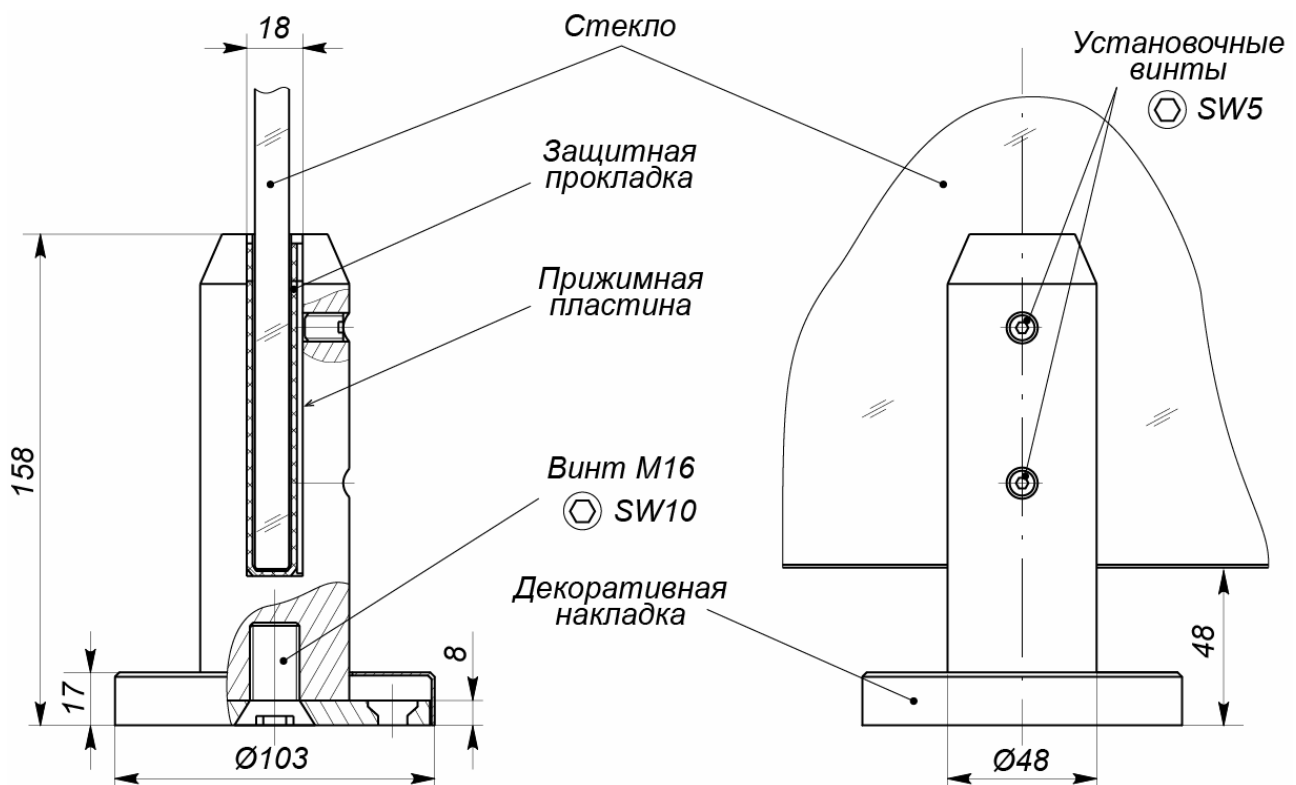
Внешний вид и размеры мини-стойки PERCo-BH06 2-00
